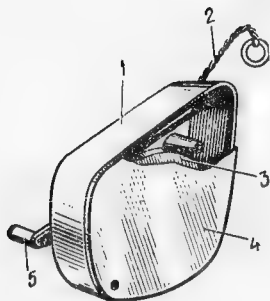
1 — корпус; 2 — шнур с кольцом; 3 — барабан; 4 — крышка; 5 — ручка
